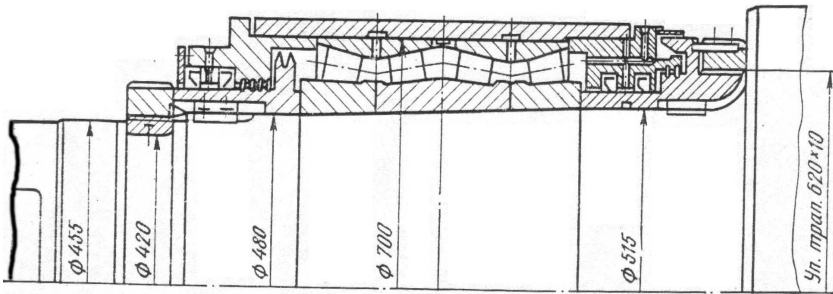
Установка рабочего валка з конічною шийкою чотиривалкового стану 2000 на роликових конічних підшипниках.
